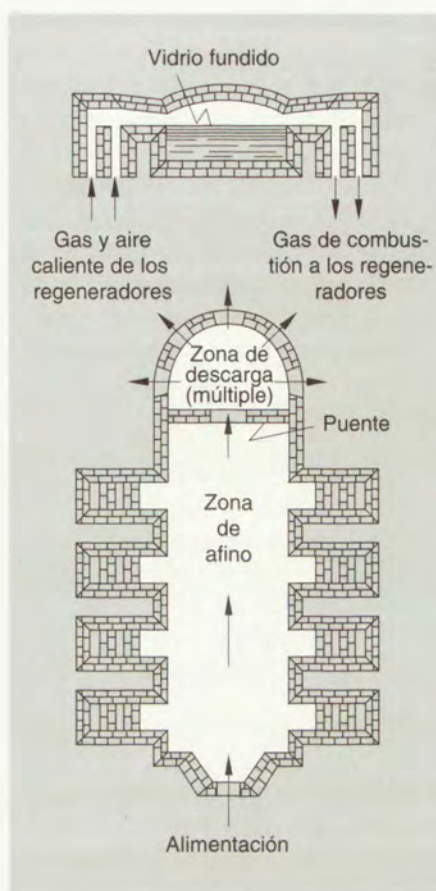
Horno vidriero de balsa, continuo. Vista en planta (abajo) y en sección vertical (arriba).
